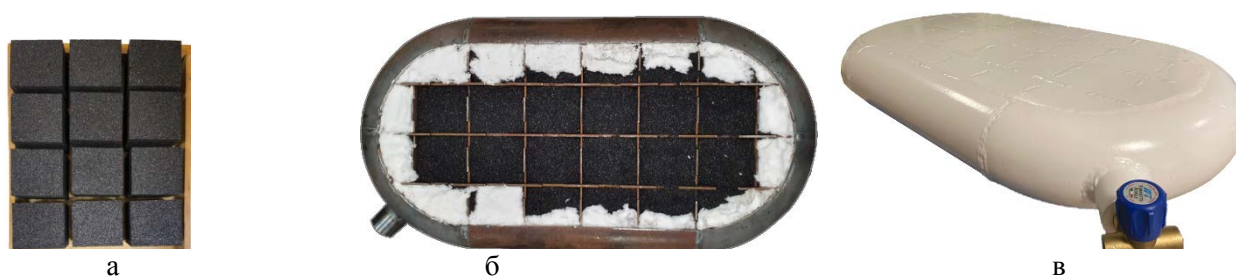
Образцы компактированного нанопористого активного угля (а); конформный бак сотовой конструкции в процессе укладки моноблоков (б); изготовленный конформный бак в процессе испытаний.
